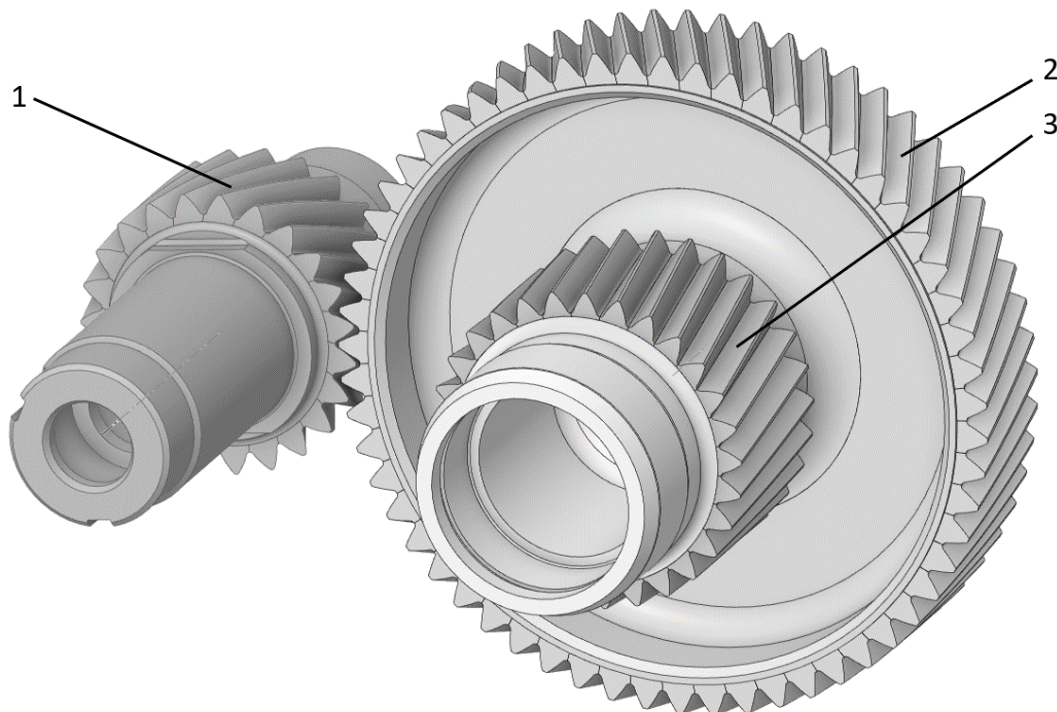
Сборка: 1 – зубчатое колесо z23, 2 – зубчатое колесо z59, 3 – зубчатое колесо z29
